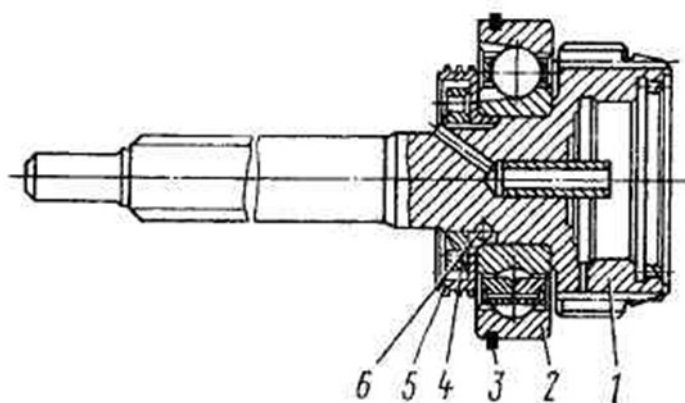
Ведущий вал коробки передач автомобиля Камаз в сборе
